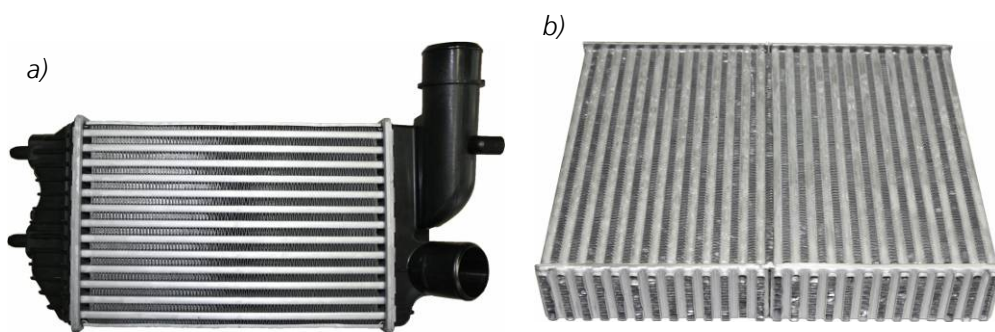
a) kompletter Ladeluftkühler b) 2 verschweißte Ladeluftkühler
